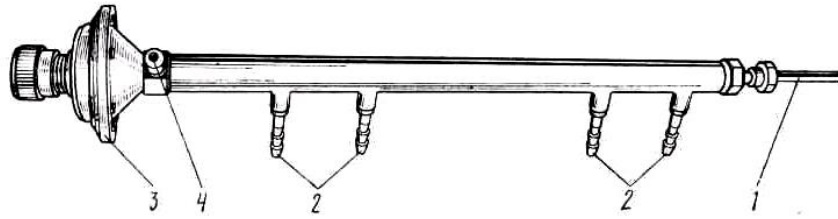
Паливний колектор зі стабілізатором тиску
